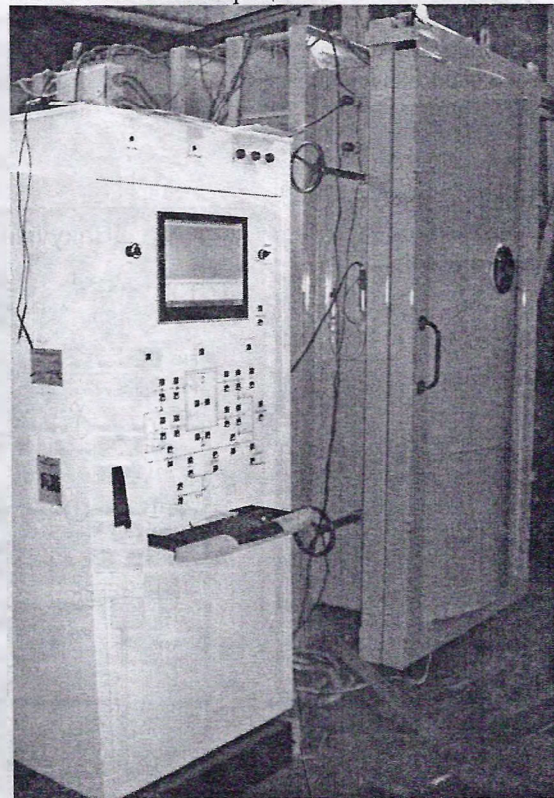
Установка VATT 1600x2400-ЭД. Вид спереди
